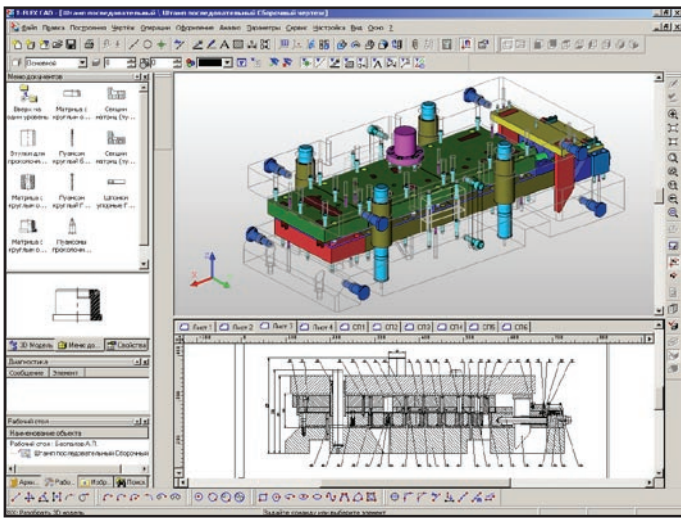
Общая 3D сборка штампа с листами чертежей.
